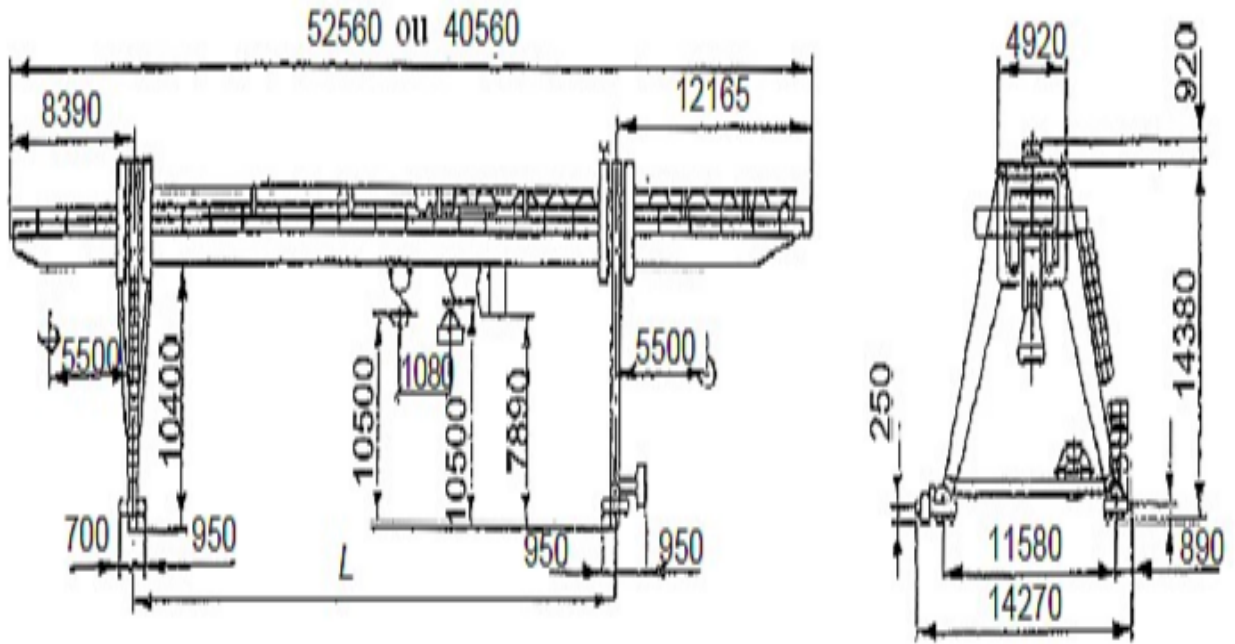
Vue d'ensemble d'une grue Portique, dimensionnement.
